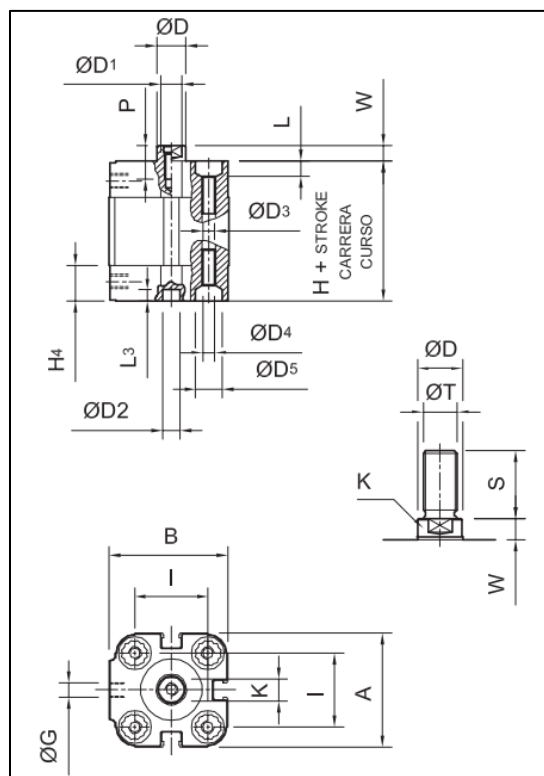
Desenho com principais dimensões do cilindro Prensa [20].
